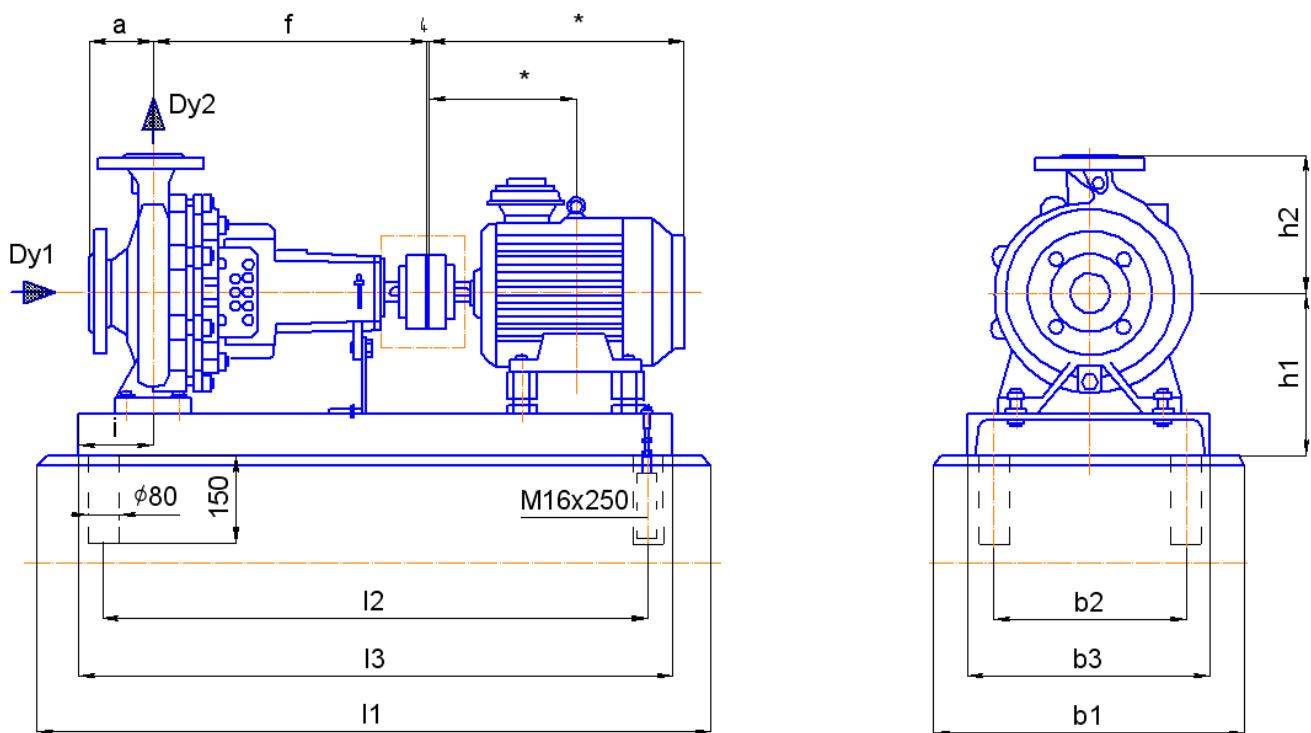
Габаритные и присоединительные размеры Иртыш – ЦНК.
